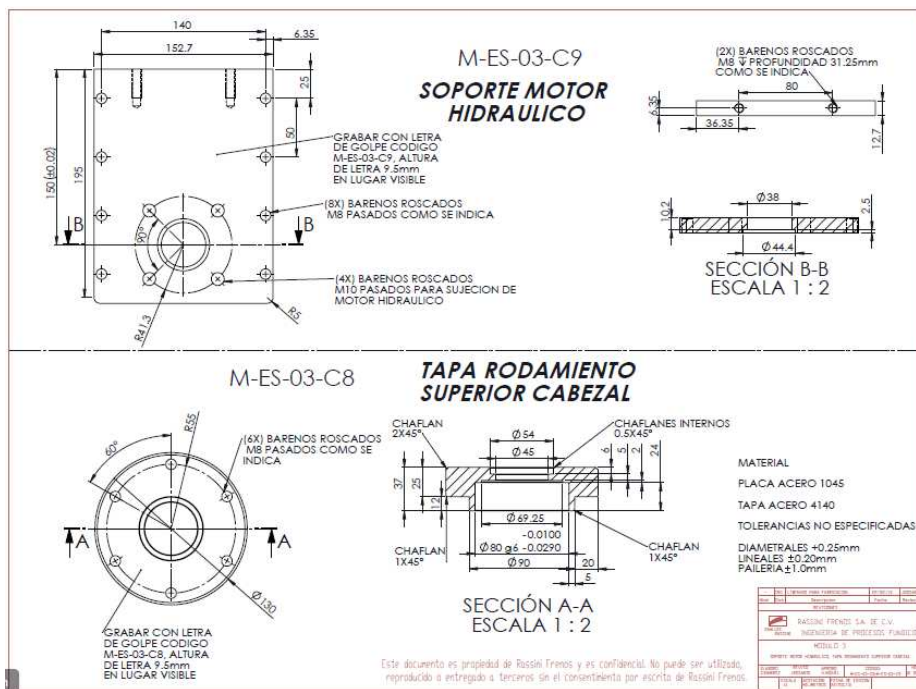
Plano de fabricación soporte motor y tapa de rodamiento
